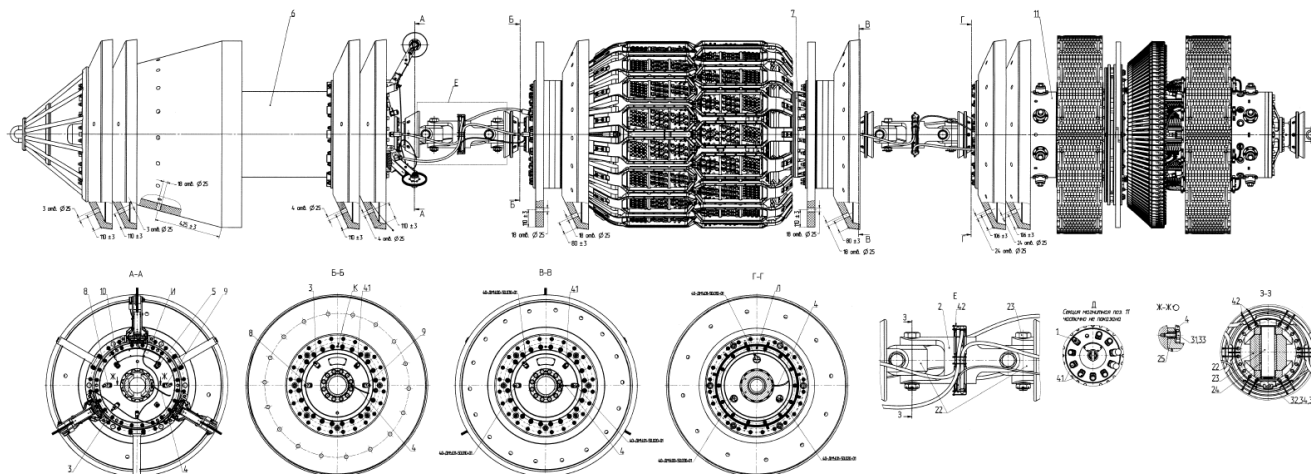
Чертеж общего вида дефектоскопа внутритрубного комбинированного магнитно-ультразвукового 40-ДМУ.01-00.000 в типоразмере 1220 мм (48")
